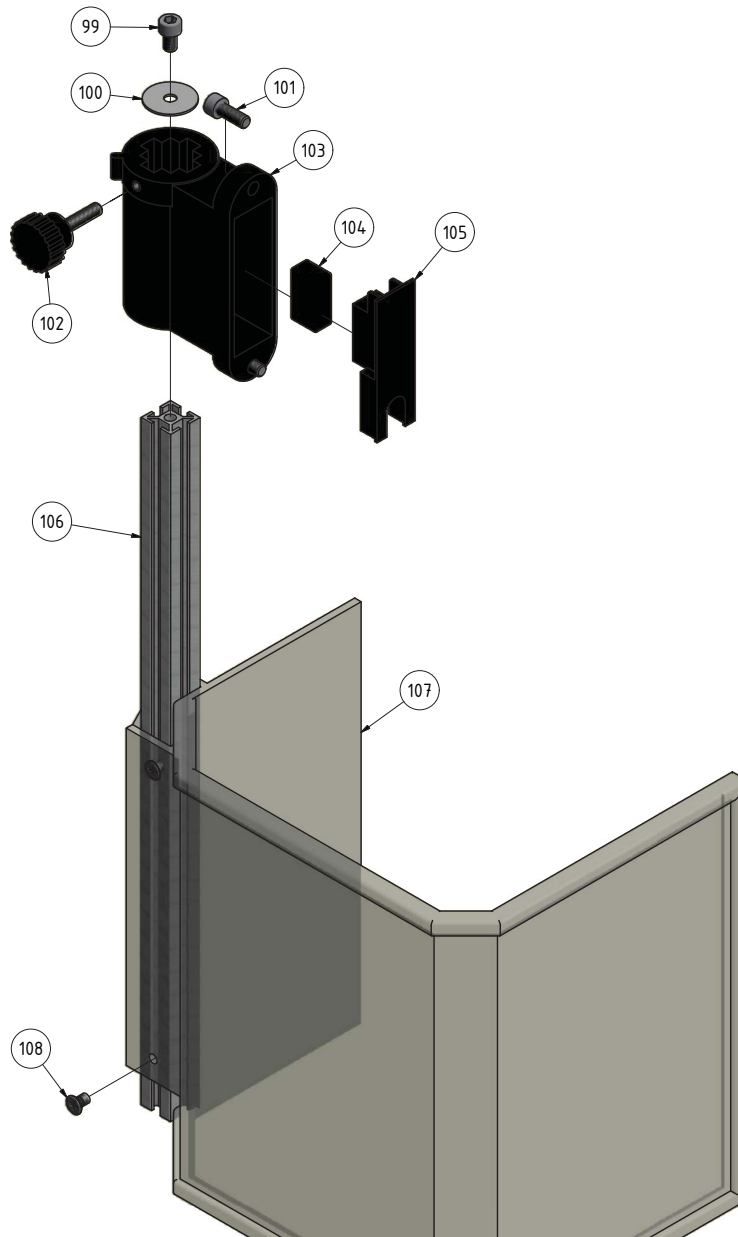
Bohrfutterschutz- Drilling chuck protection
